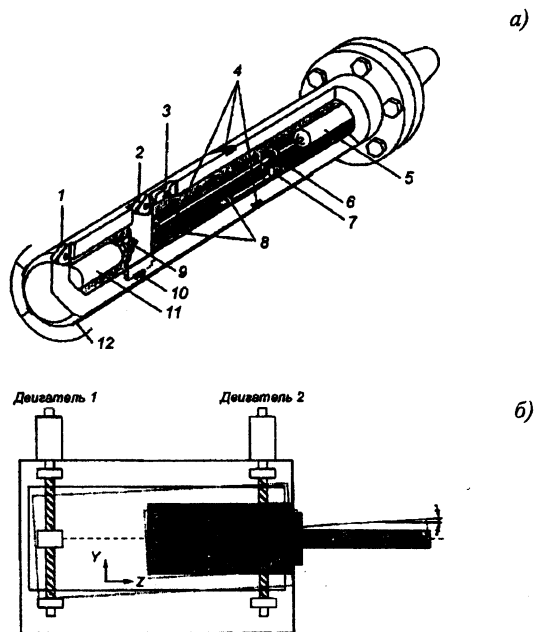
Схема оправки с адаптивным управлением (а) и устройства для компенсации положения вершины резца (б) [6]
